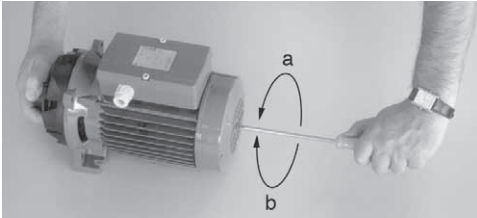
Smontaggio (a) e rimontaggio (b) girante
